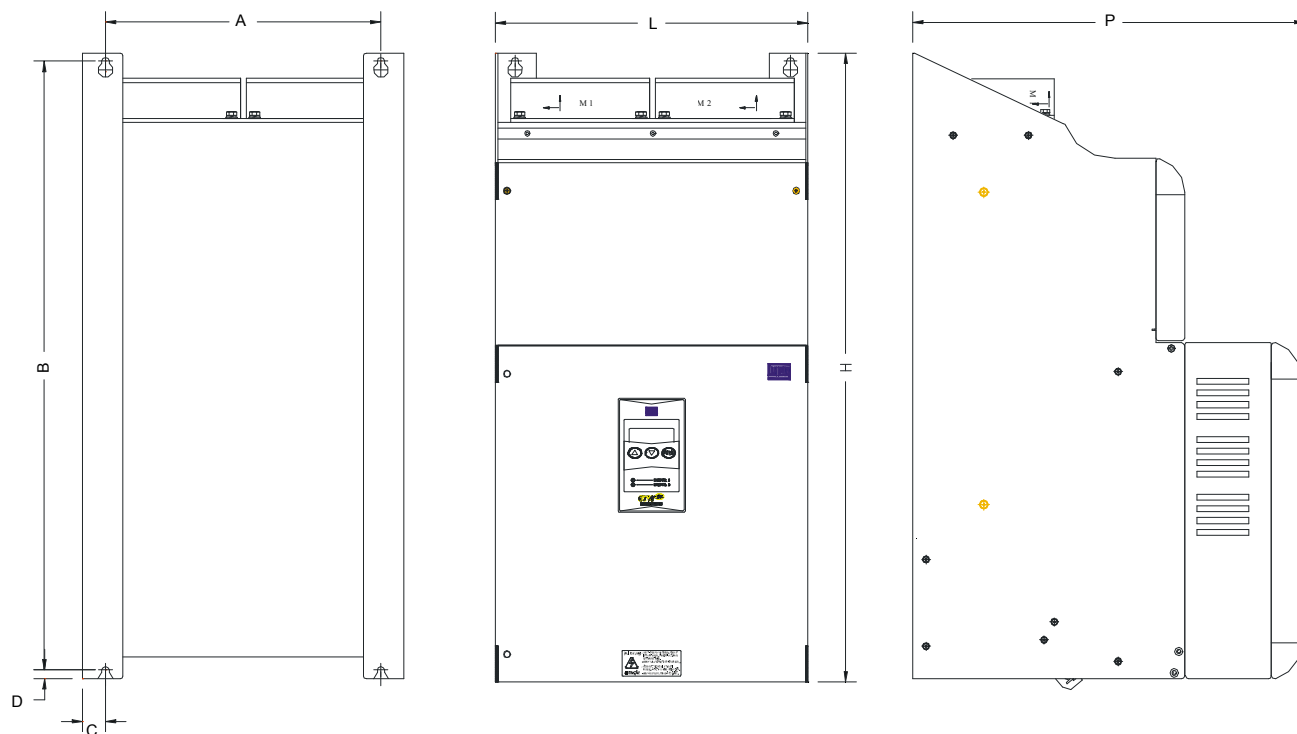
c) – Dimensional do Conversor CTW-04 - Mec 03
